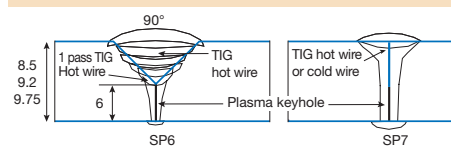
SP7 Vorteile beim Schweißen dicker Bleche oder Rohre
